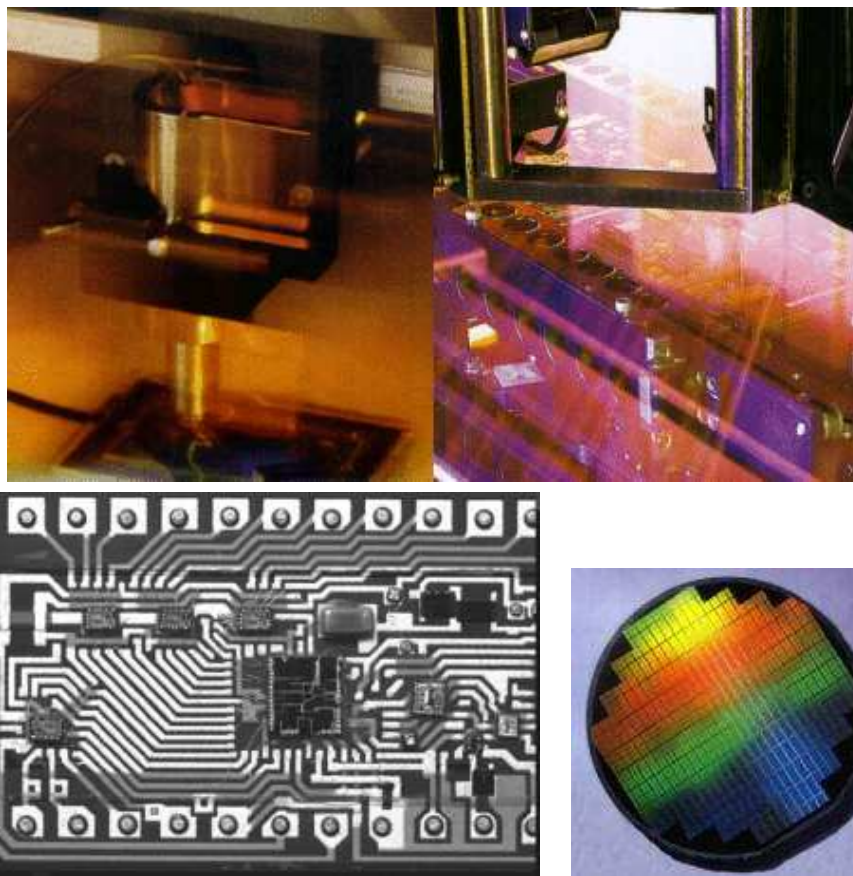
Fabrication de composants électroniques: découpage du *wafer*, placement des *dies* et soudage des contacts.
